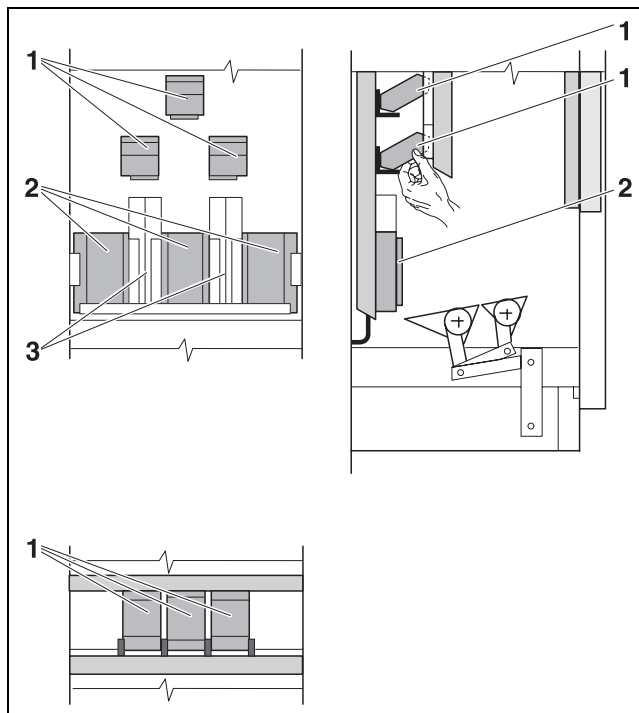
Wkładanie kształtek szamotowych w przypadku typów 12, 16
